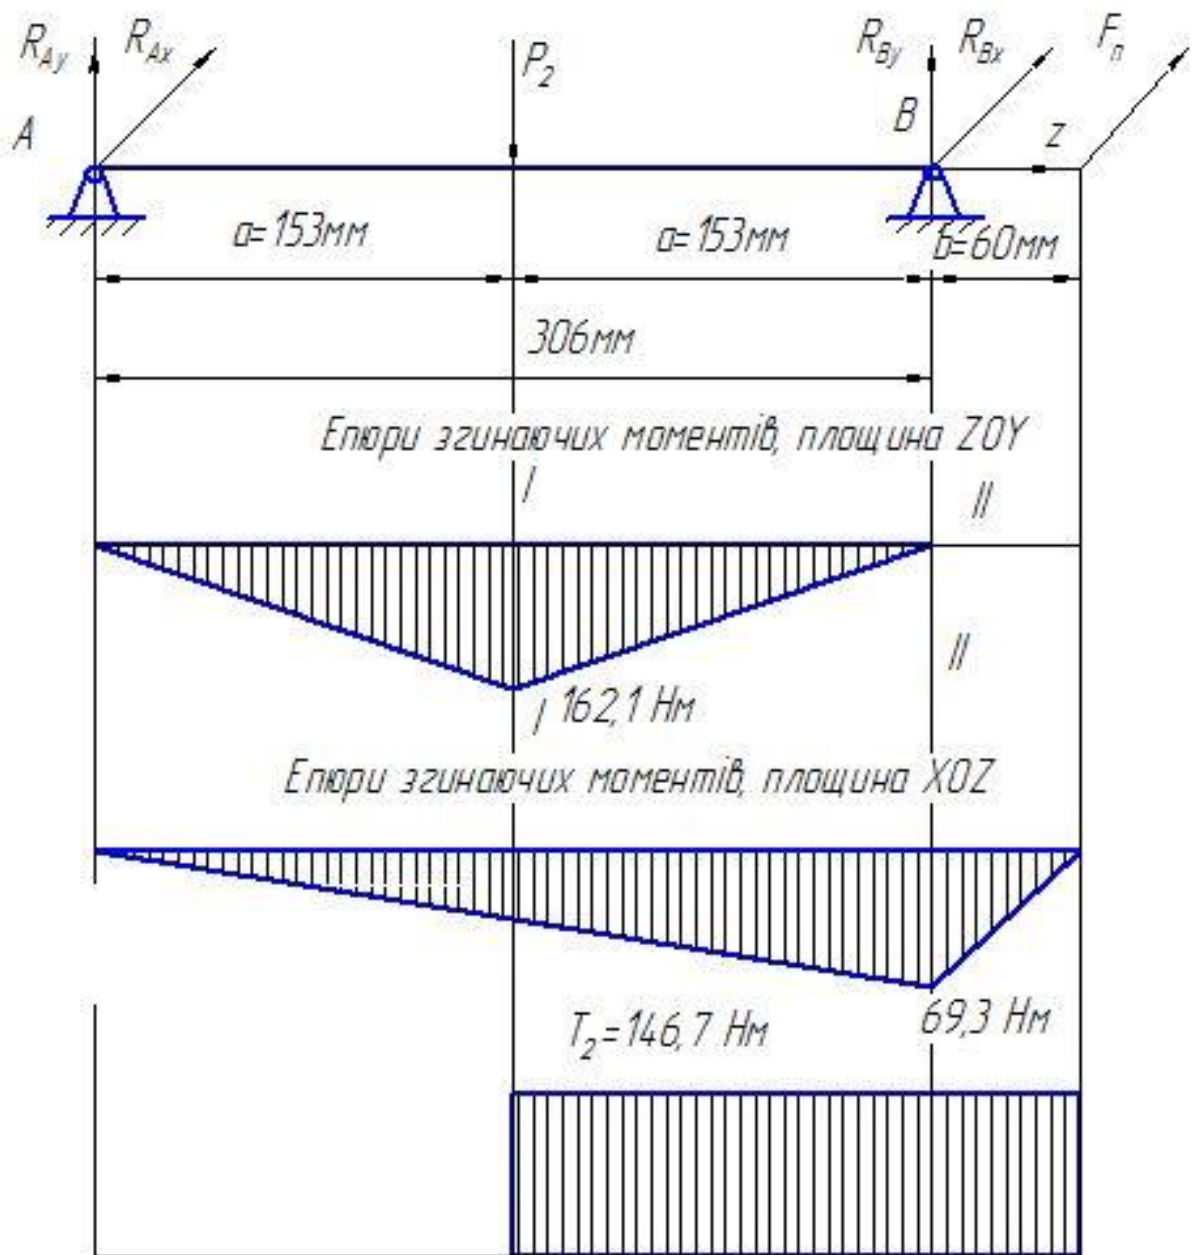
Розрахункова схема ведучого вала транспортера
